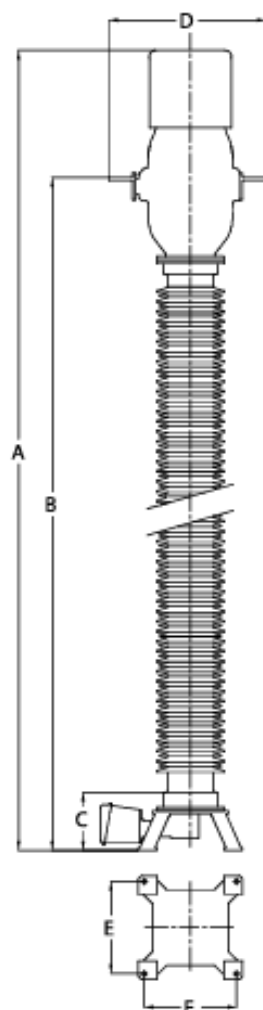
Габаритні креслення роз'єднувача S2DA 123
